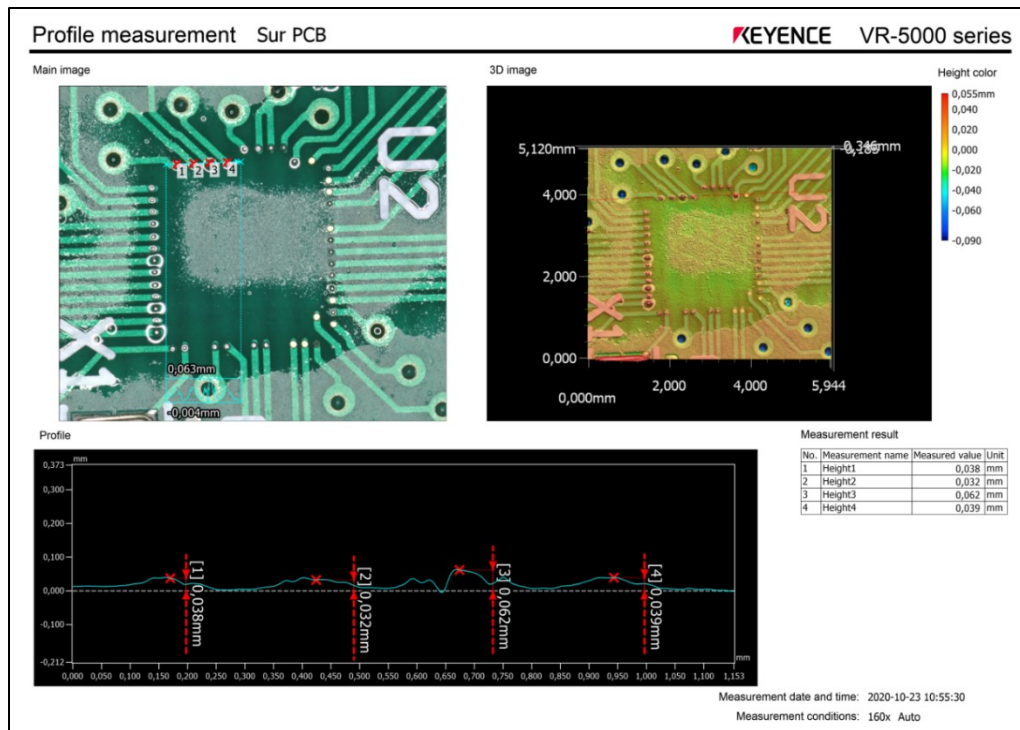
Vue des *solderbumps* sur le PCB après la tentative d'assemblage de l'ASIC
